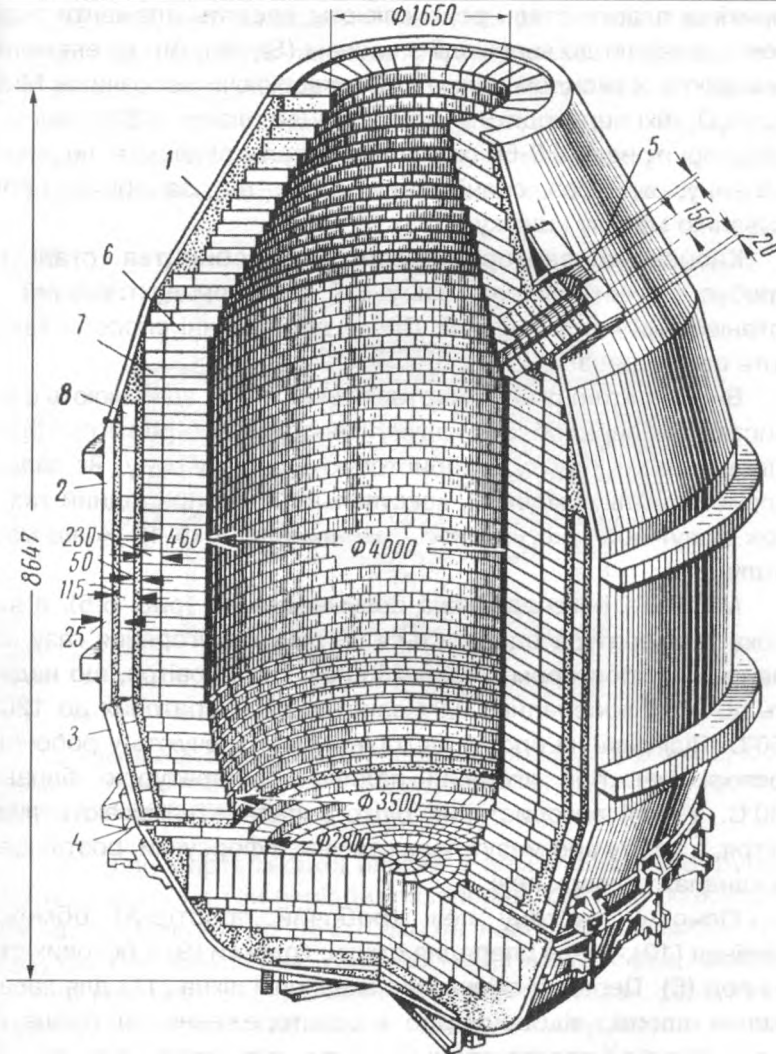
Корпус кисневого конвертера з футеровкою: 1 - шльомна частина; 2 - циліндричний пояс; 3 - нижній зрізаний конус; 4 - кільце; 5 - сталевипускний отвір; 6 - робочий шар футеровки; 7 - проміжний шар футеровки; 8 - арматурний шар
